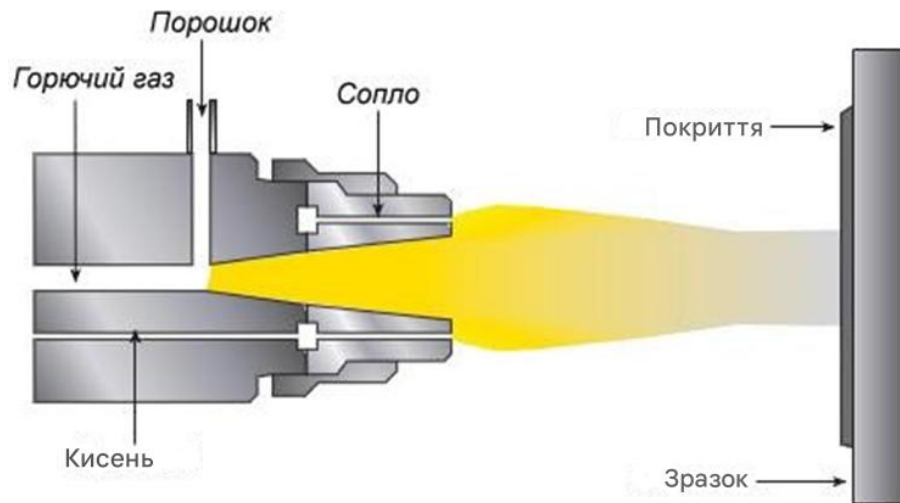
Схема процесу газополум'яного напилення деталей
